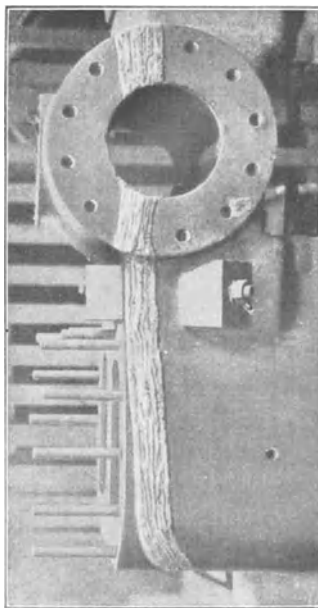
Gußzylinder, fertig geschweißt.
